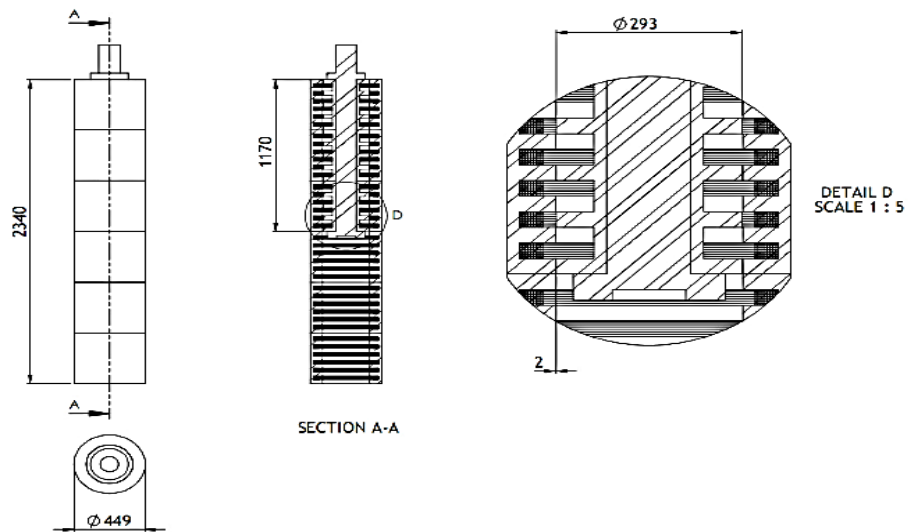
Dimensões finais do gerador linear tubular (mm) [21]
